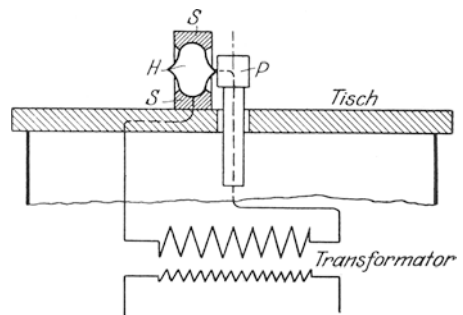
Schema der Hohlkörperschweißung.
